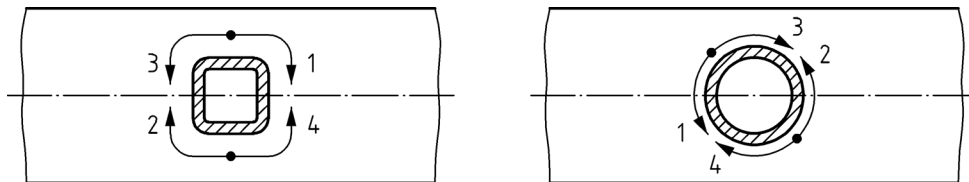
Точки початку наплавлення зварного шва та точки зупини й послідовність зварювання
